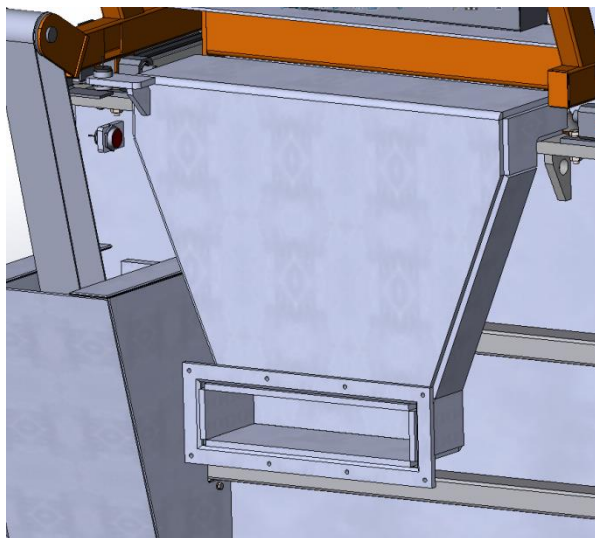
Вентиляционный зонт установки покрытия насыпью
